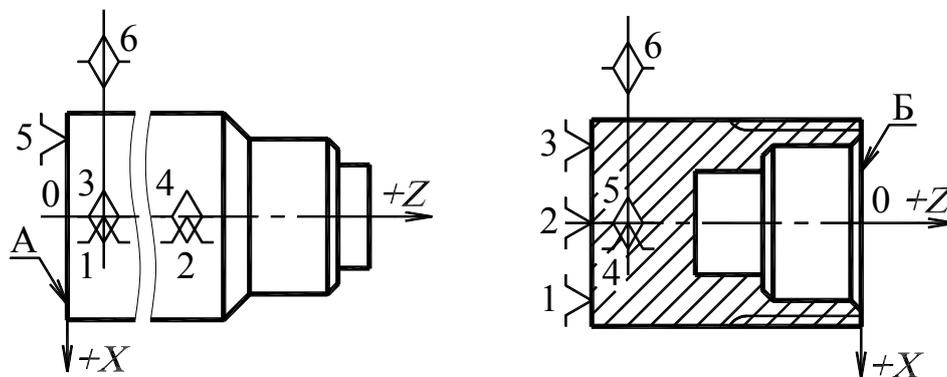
Варианты выбора начала системы координат заготовки (детали)
